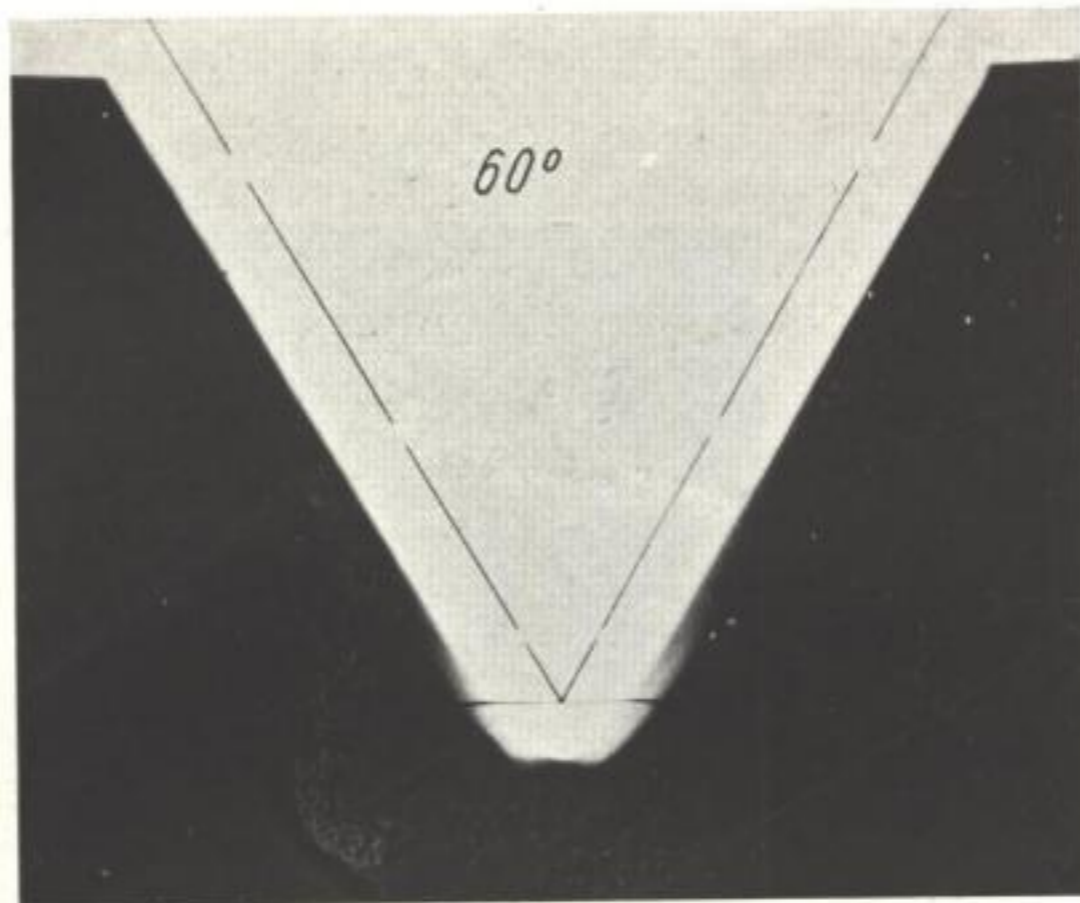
Ungenaue Abbildung des Gewindekernes durch zu hohe Apertur der beleuchtenden Strahlen. Werkphoto Lindner, phot. Dr. STADE.
